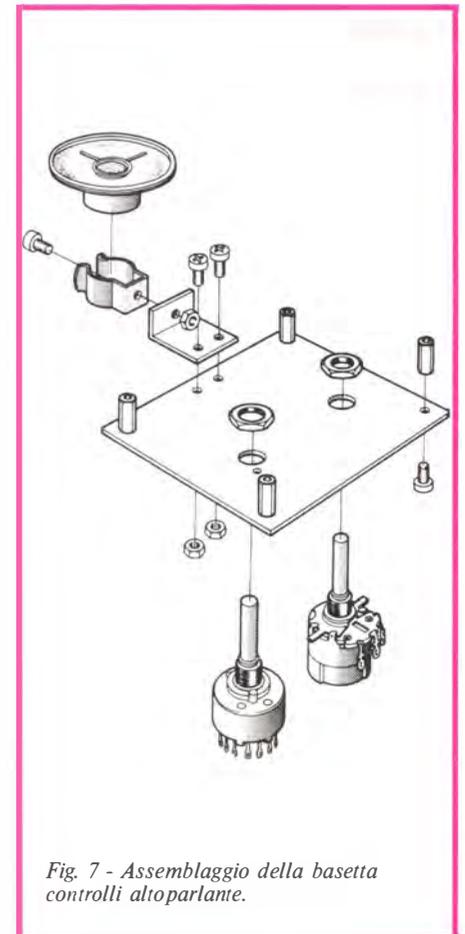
Assemblaggio della basetta controlli altoparlante.
